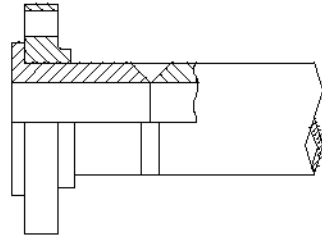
Diseño del bisel en la junta de soldadura para tubos de igual espesor de pared.
